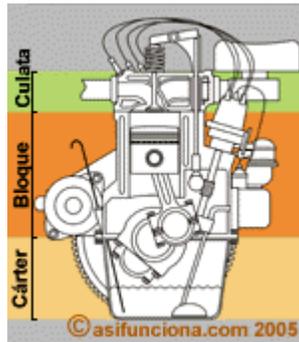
Partes principales en las que se divide un motor de gasolina.<sup>80</sup>
